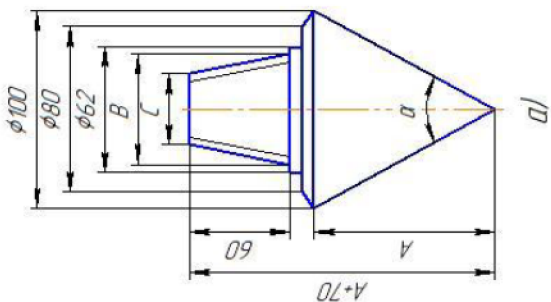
Інструмент для ударно-вібраційного зондування
